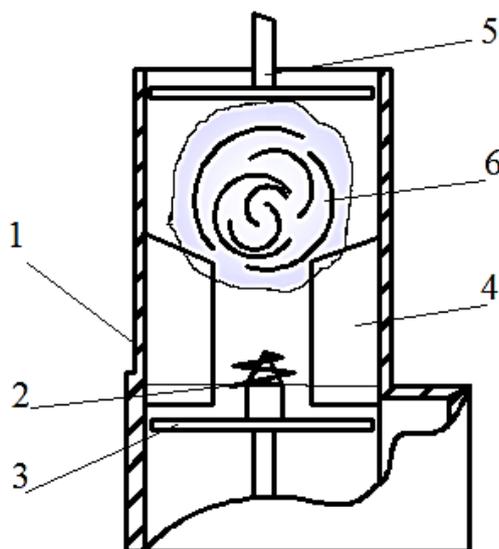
Пристрій для шаткування капусти: 1-корпус, 2-свердло, 3-опорний диск з ножами, 4-ребра-леза, 5-проштовхувач, 6 - качан капусти
